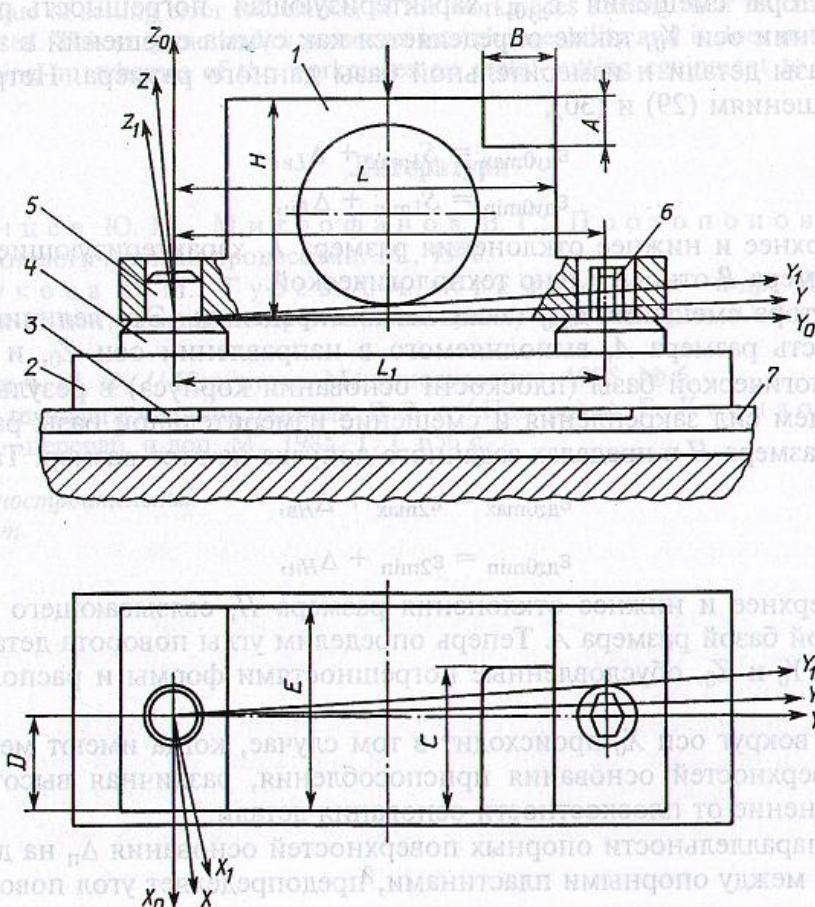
Схема для расчета погрешностей установки при базировании корпусной детали по плоскости и двум отверстиям: 1 — деталь; 2 — основание приспособления; 3 — направляющая шпонка; 4 — опорная пластина; 5 — палец цилиндрический; 6 — палец срезанный; 7 — стол станка
